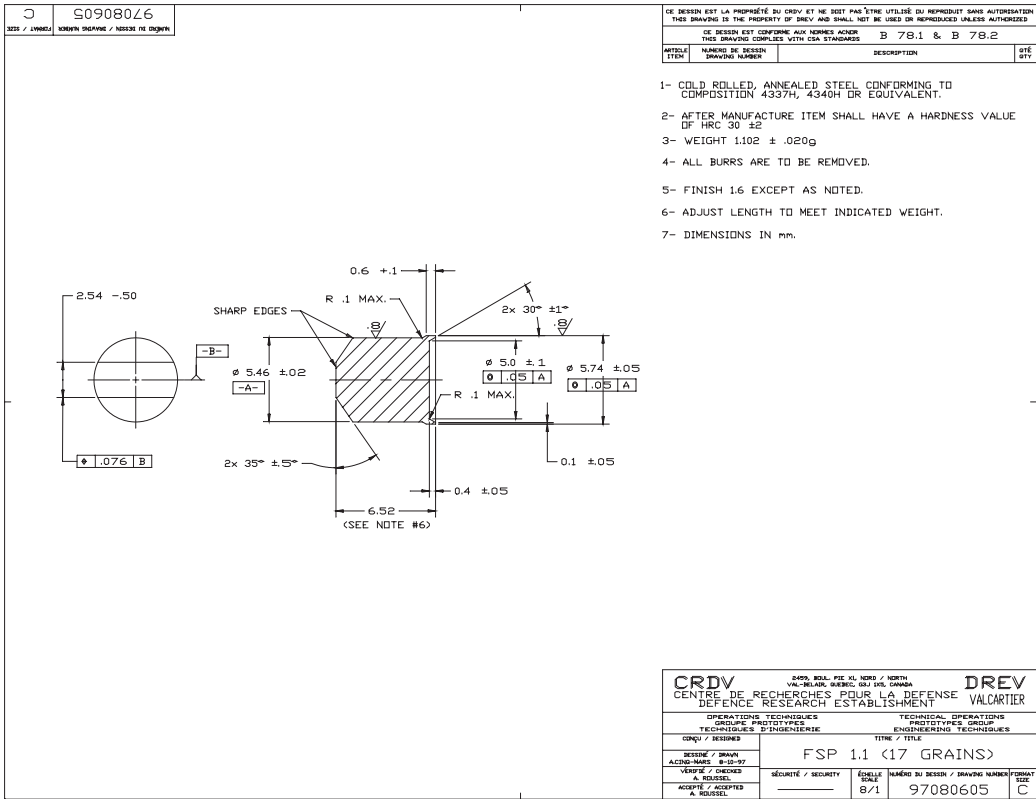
Dimensions du projectile à simulation de fragment (PSF)
